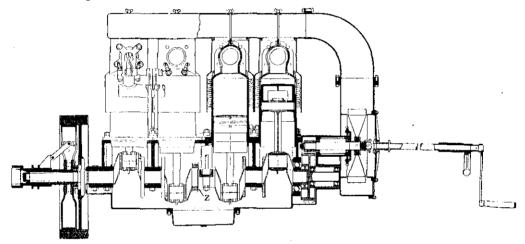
Охлаж дающійся воздукомь дингатель Фрайеръ-Миллера.
